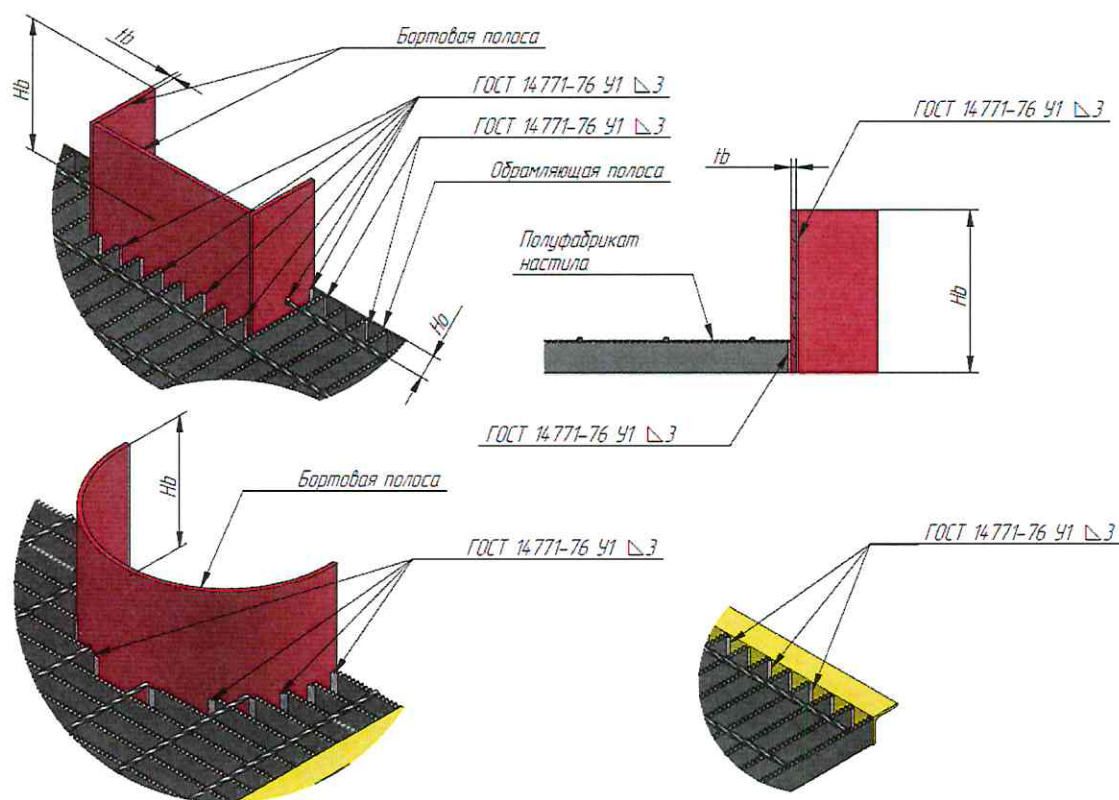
Пример выполнения сварки обрамляющего уголка и бортовой полосы.
